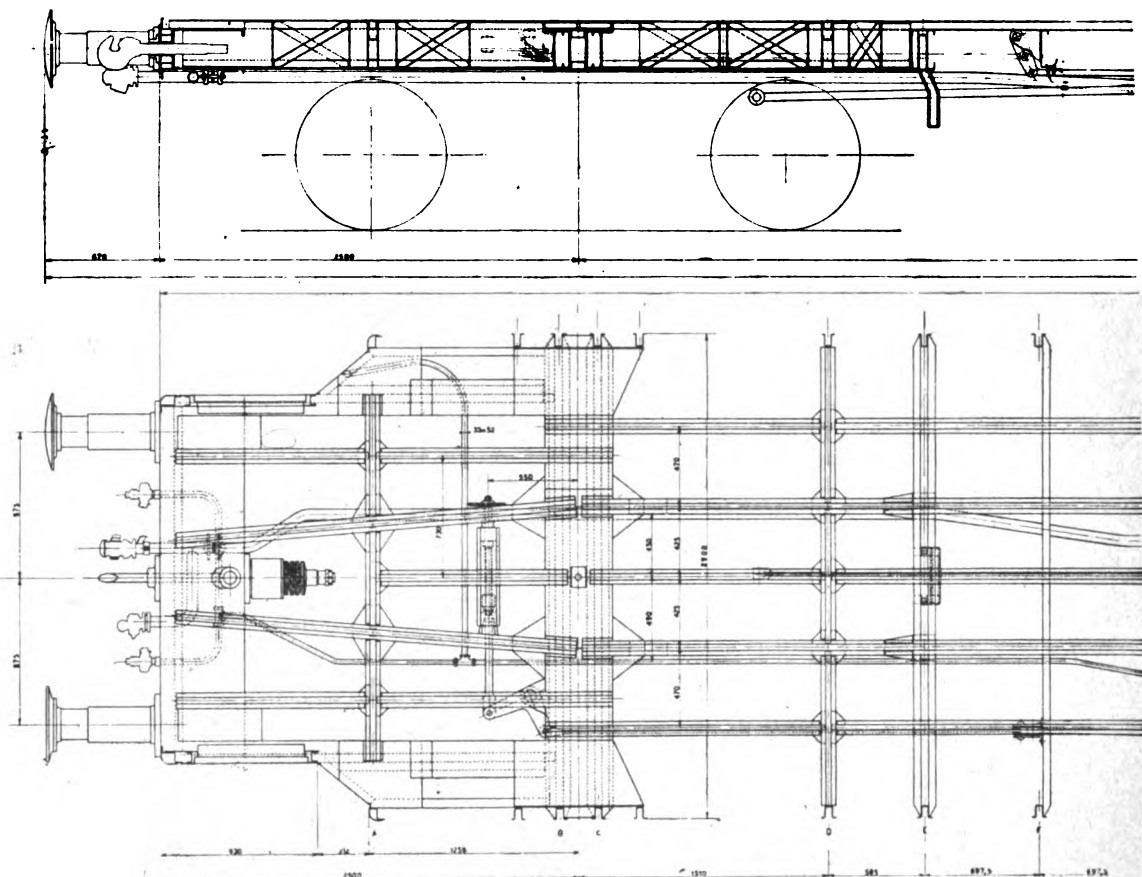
Traversa di testa, trave portaralla e loro collegamenti
